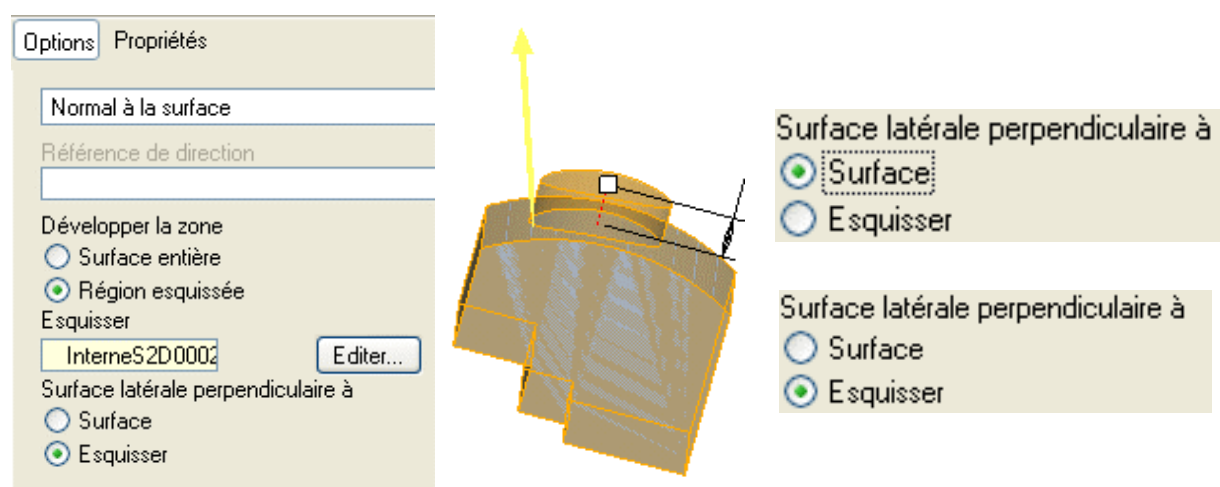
Décalage solide surface latérale perpendiculaire à surface ou esquissée.
